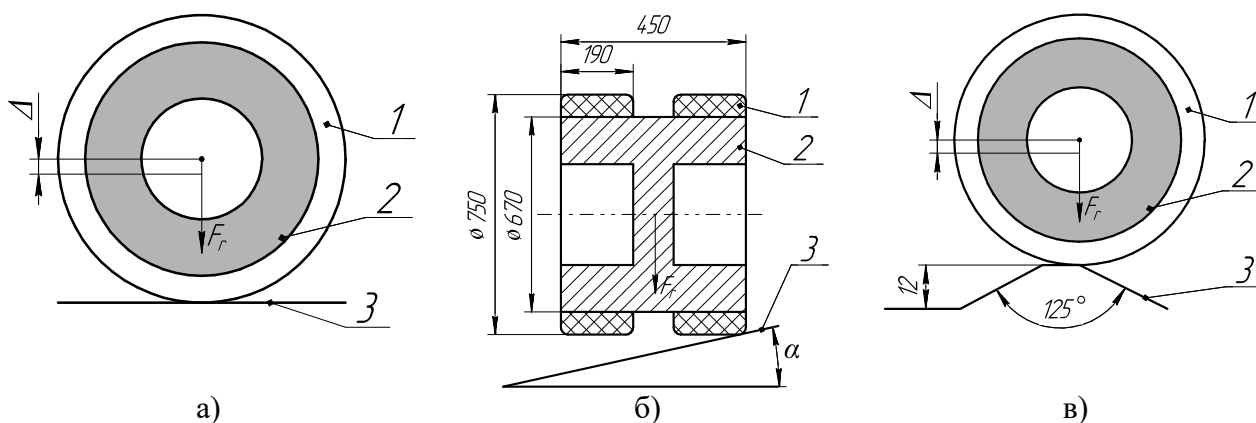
Расчетные схемы нагружения резиновой шины опорного катка
